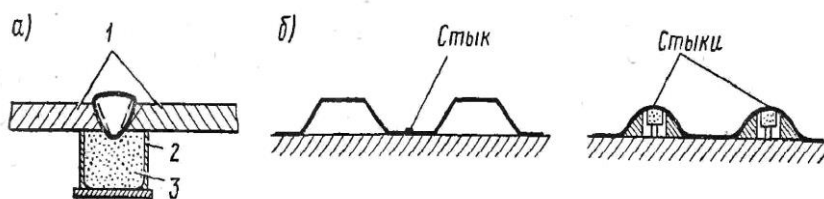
Способы сварки стыковых соединений:
